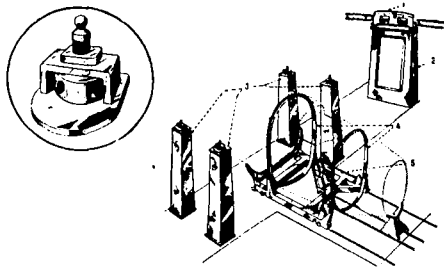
Детали приспособления, на котором выполняется сборка носовой части фюзеляжа с нижней панелью. На эскизе показаны детали нижнего бандажа, установленного в приспособлении для сборки
